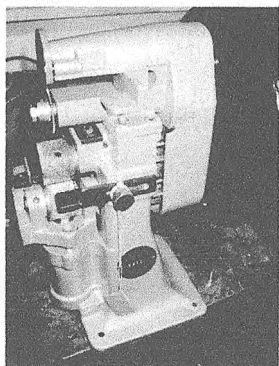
Приспособление для двоения и обрезки деталей по периметру Rodi 50 SL фирмы Hardo (Германия)
